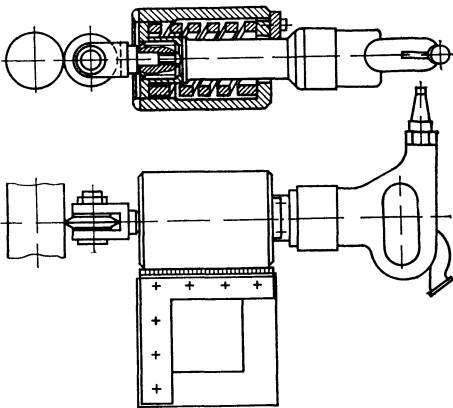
Схема чеканочного приспособления типа ЧМ-3
